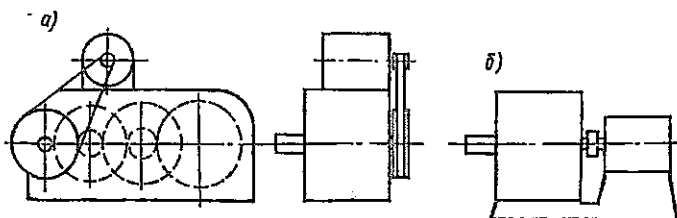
Редуктор с быстроходной ступенью, осуществленной ременной (а) и зубчатой (б) передачами
